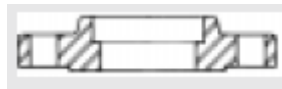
Socket Weld (para soldar embutido). [17]
